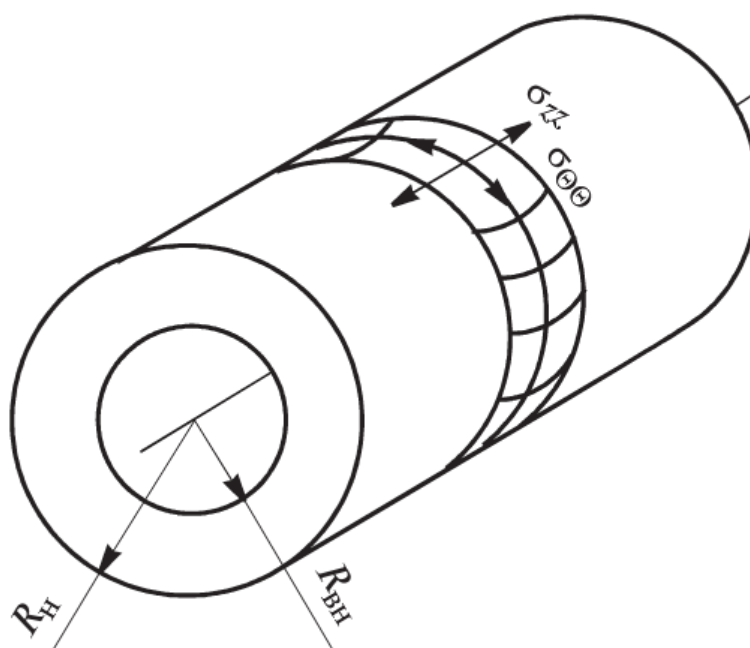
Схема напряженного состояния в стенке сварной трубы
